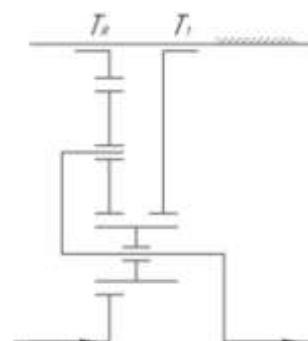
Упрощенная схема реверс-редуктора для полуоси
